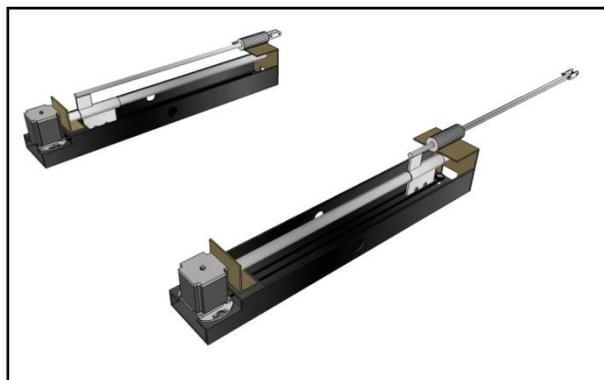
Diseño de mecanismo de apertura y cierre de puertas.
